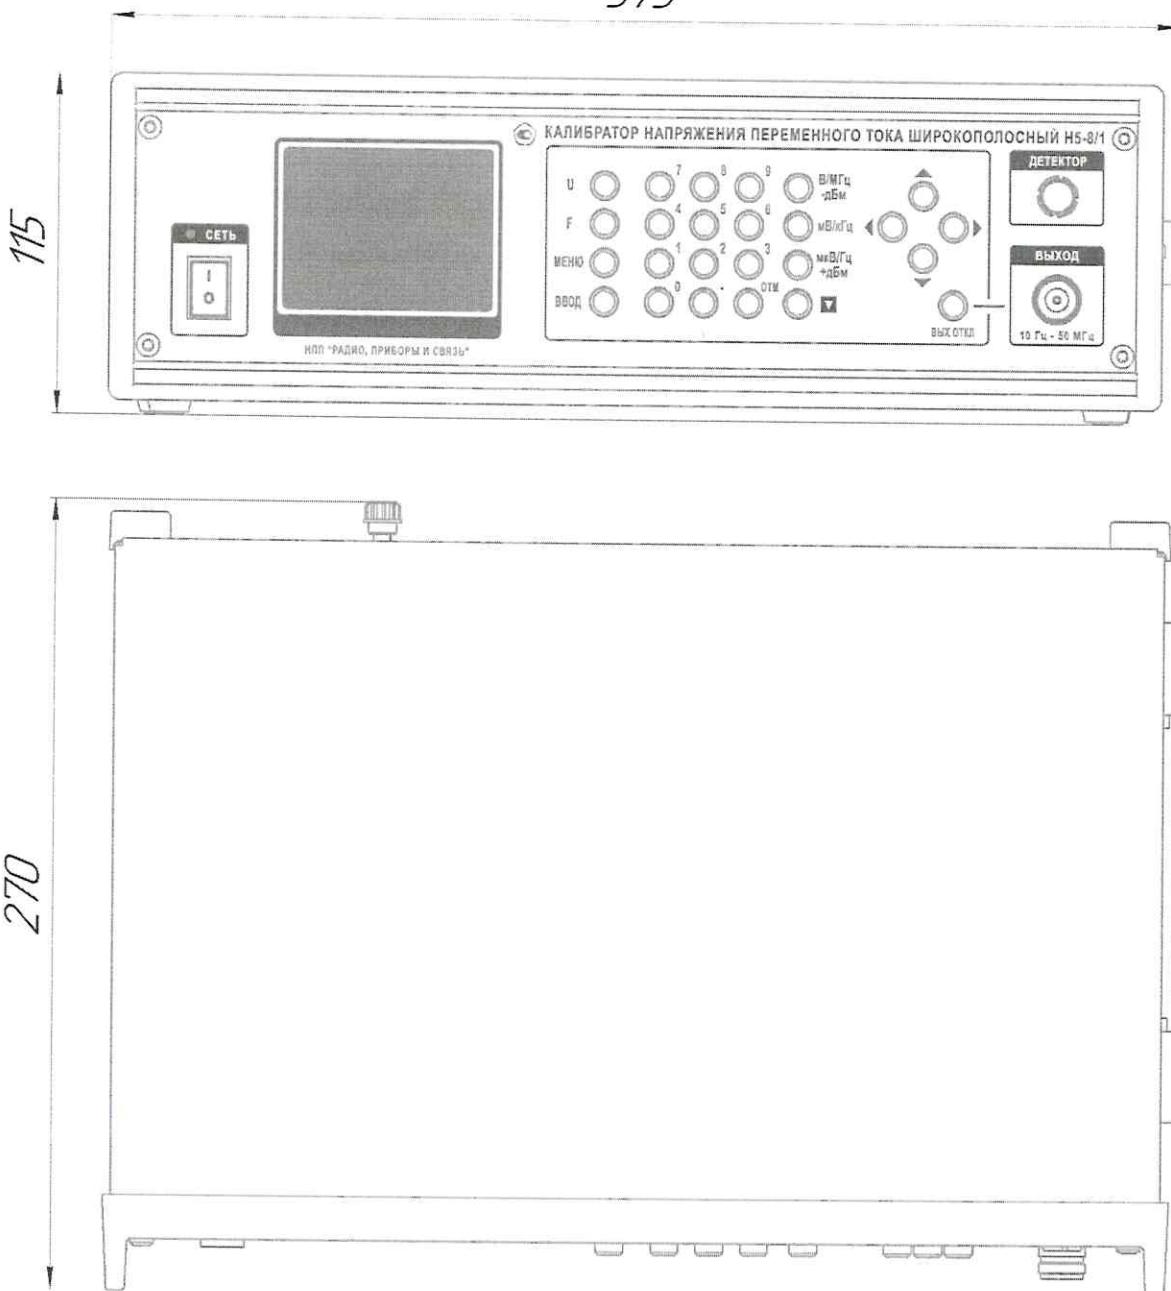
Габаритные размеры прибора Н5-8/1
